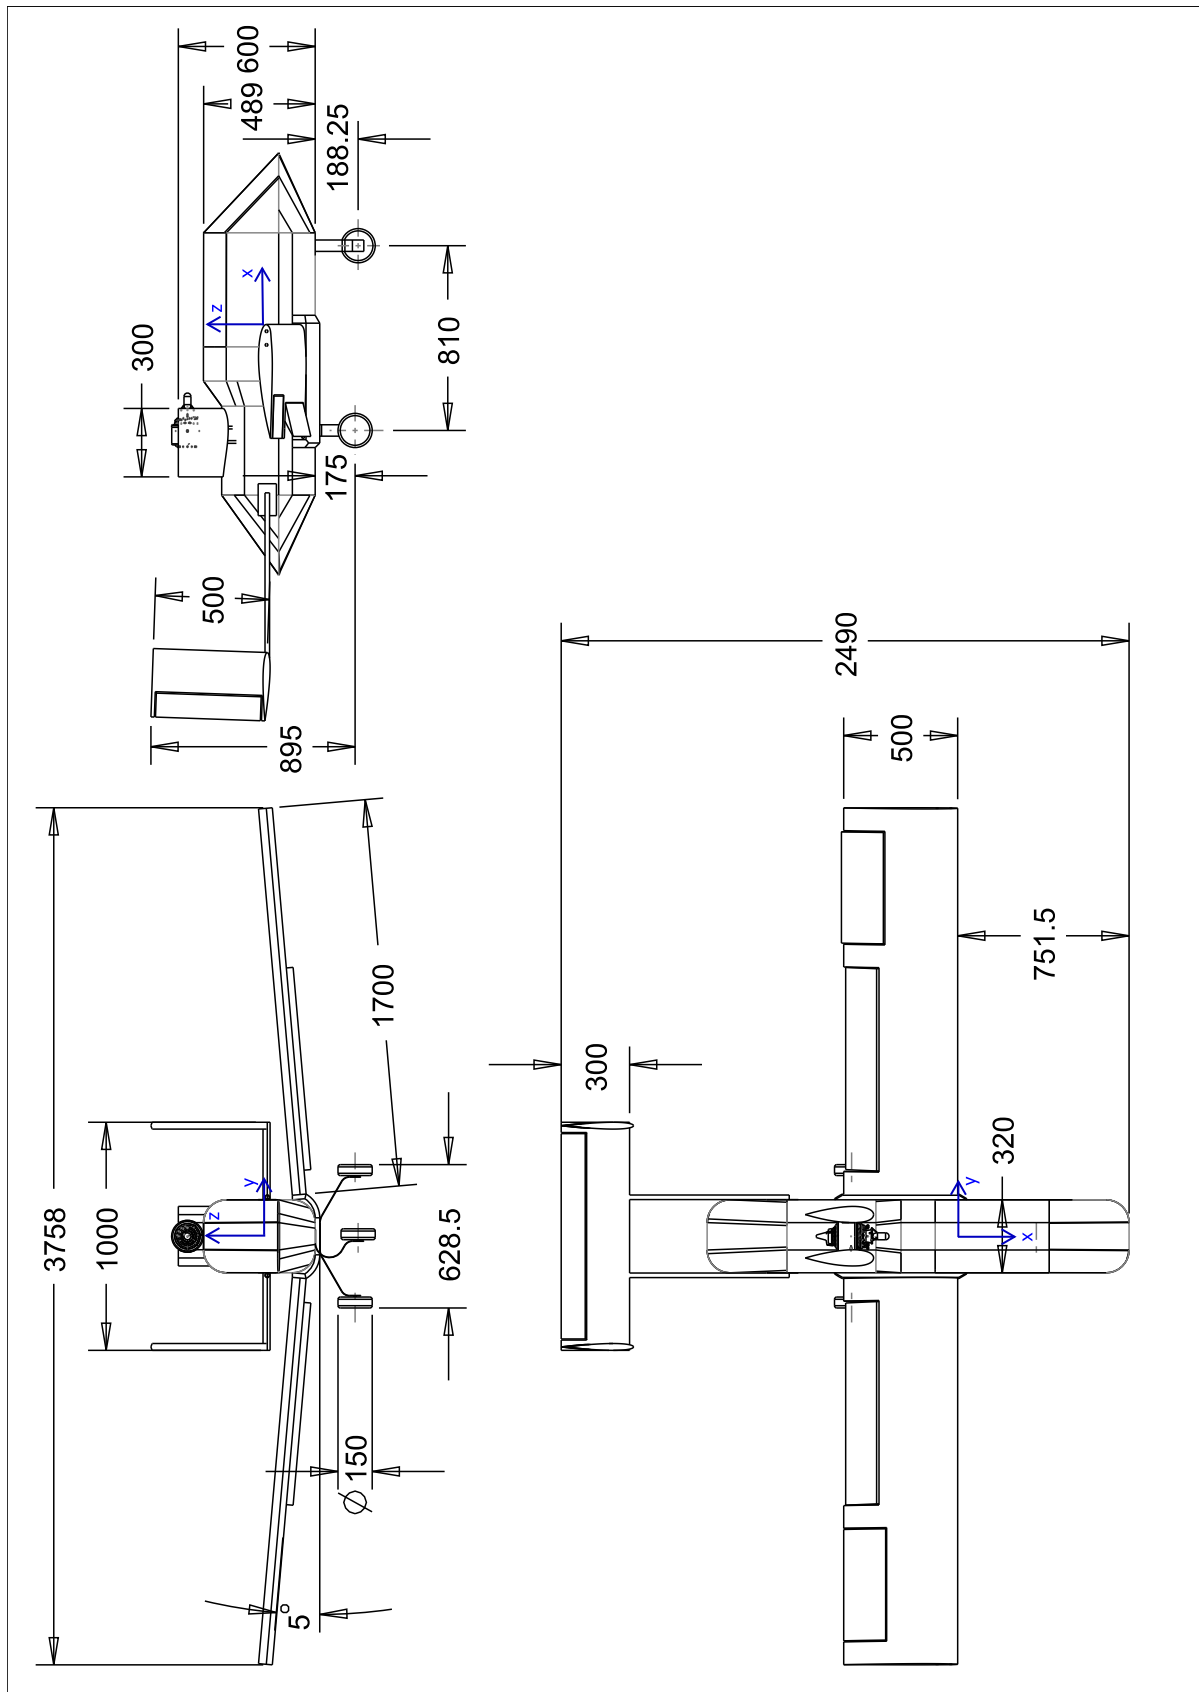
Abmessungen des Trägerflugzeuges
